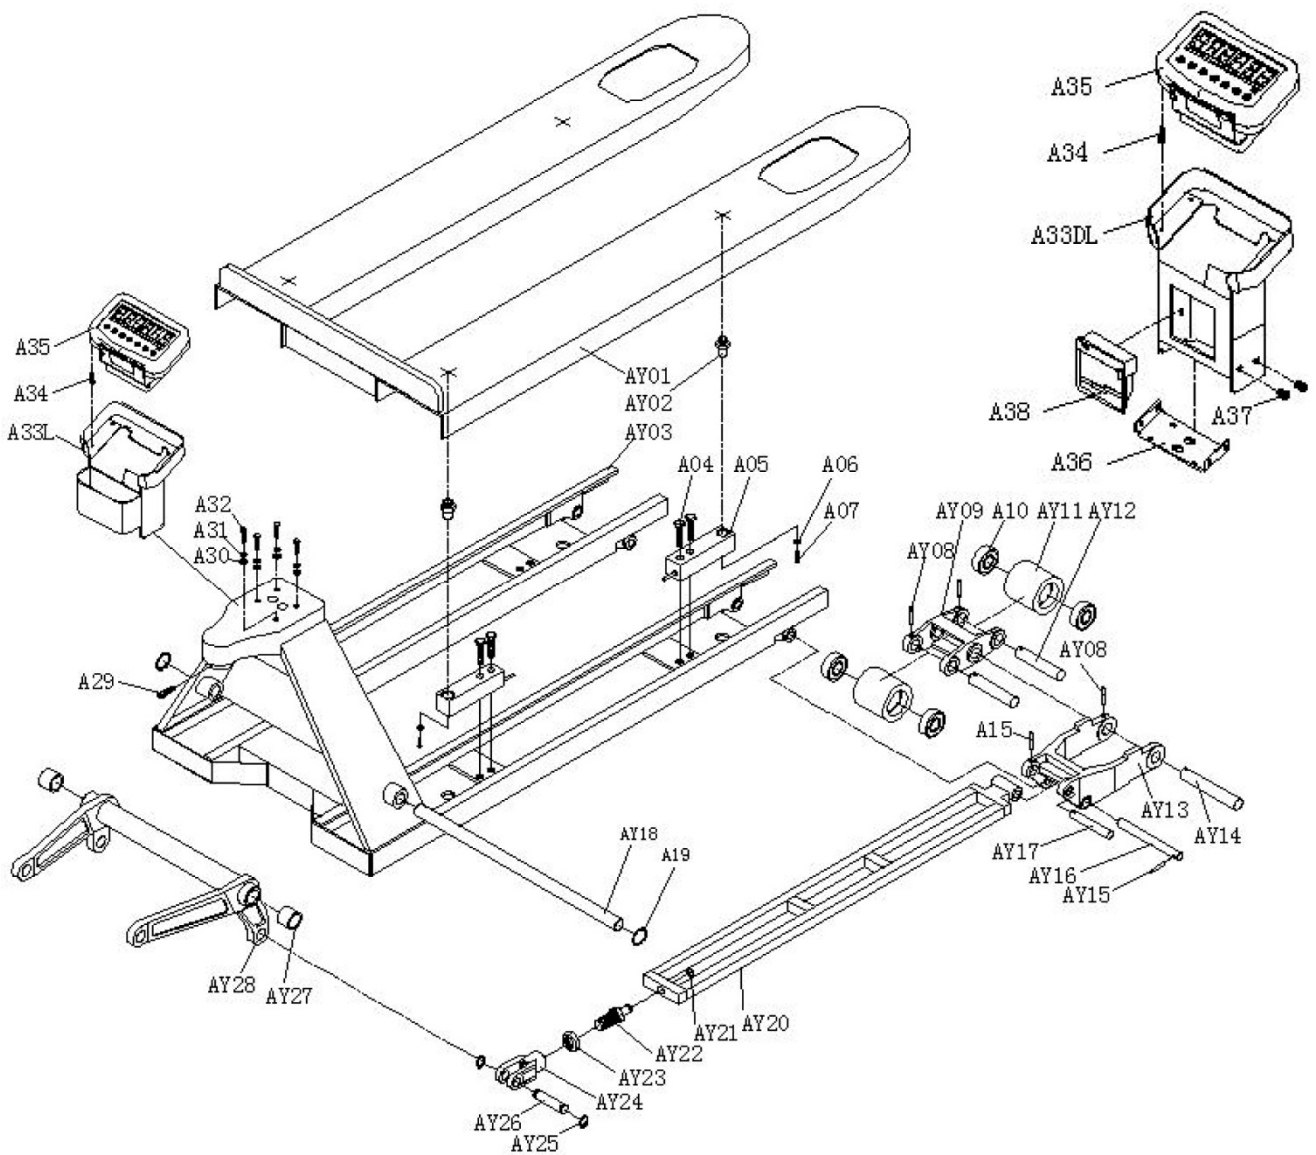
Explosionszeichnung des Gehäuses und des Druckergehäuses des Wagens WH-25ES.
